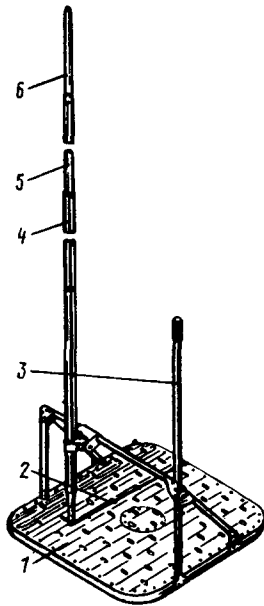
Установка для проверки соконусности лопастей несущего винта:
